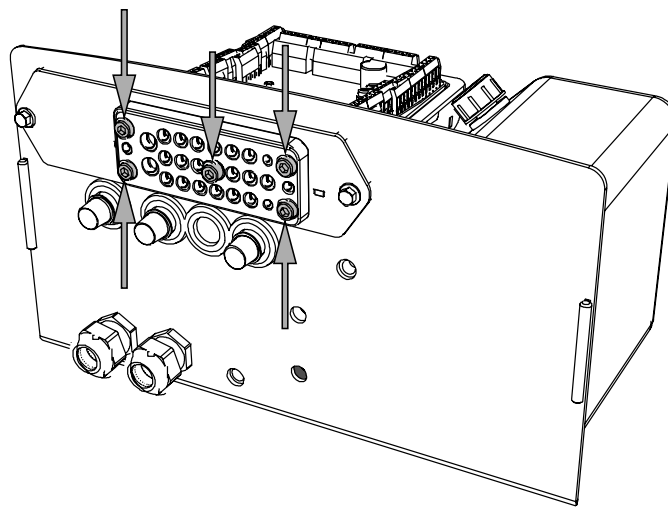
Die fünf Schrauben der Kabeldurchführung. Hydraulikaggregat 5915
